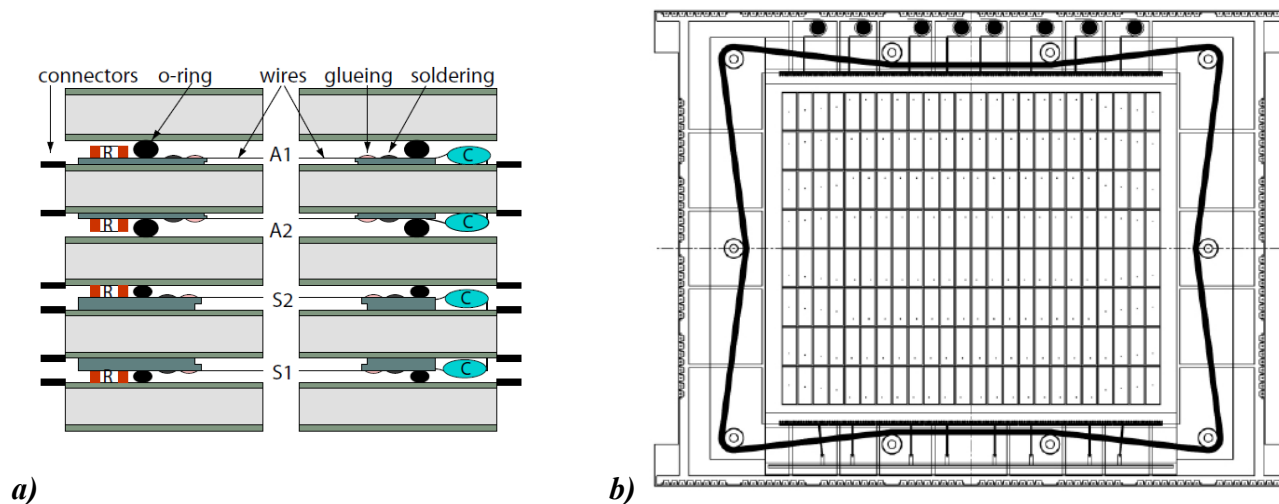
Асимметричная A1, A2 и суперсимметричная S1, S2 двухслойные камеры с размерами катодных падов 1.5×3 см², собранные в одном корпусе: зазоры камер показаны в разрезе (a); в плане – (b). Герметичность газового объема в собранной конструкции обеспечивается резиновым жгутом (*O-ring*).
